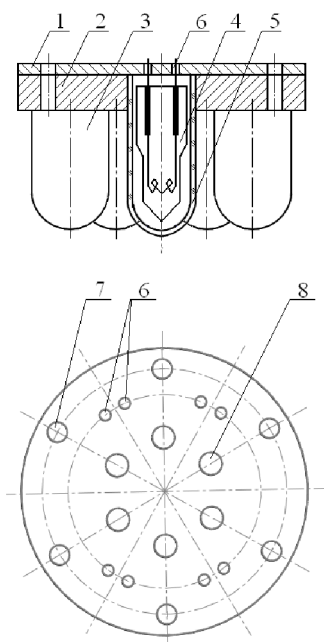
Конструктивная схема оптического наконечника семилампового излучателя для проплавления канала в СЖК: 1 – текстолитовая шайба; 2 – шайба из дюралюминия с отверстиями для установки галогенных ламп; 3 – кварцевый корпус излучателя; 4 – галогенная лампа; 5 – прозрачная стенка кварцевого корпуса; 6 – отверстия для электрических проводов; 7 – отверстия для крепления шайб; 8 – отверстия для пропускания жидкой фазы
